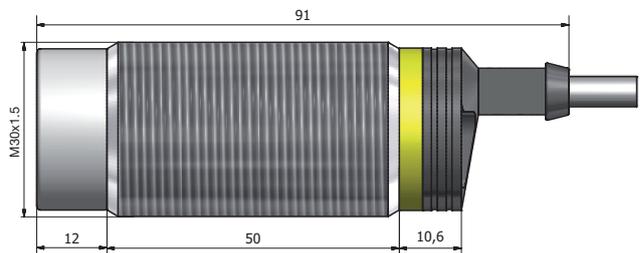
Kurze Ausführung, bündiger Einbau, Steckversion
